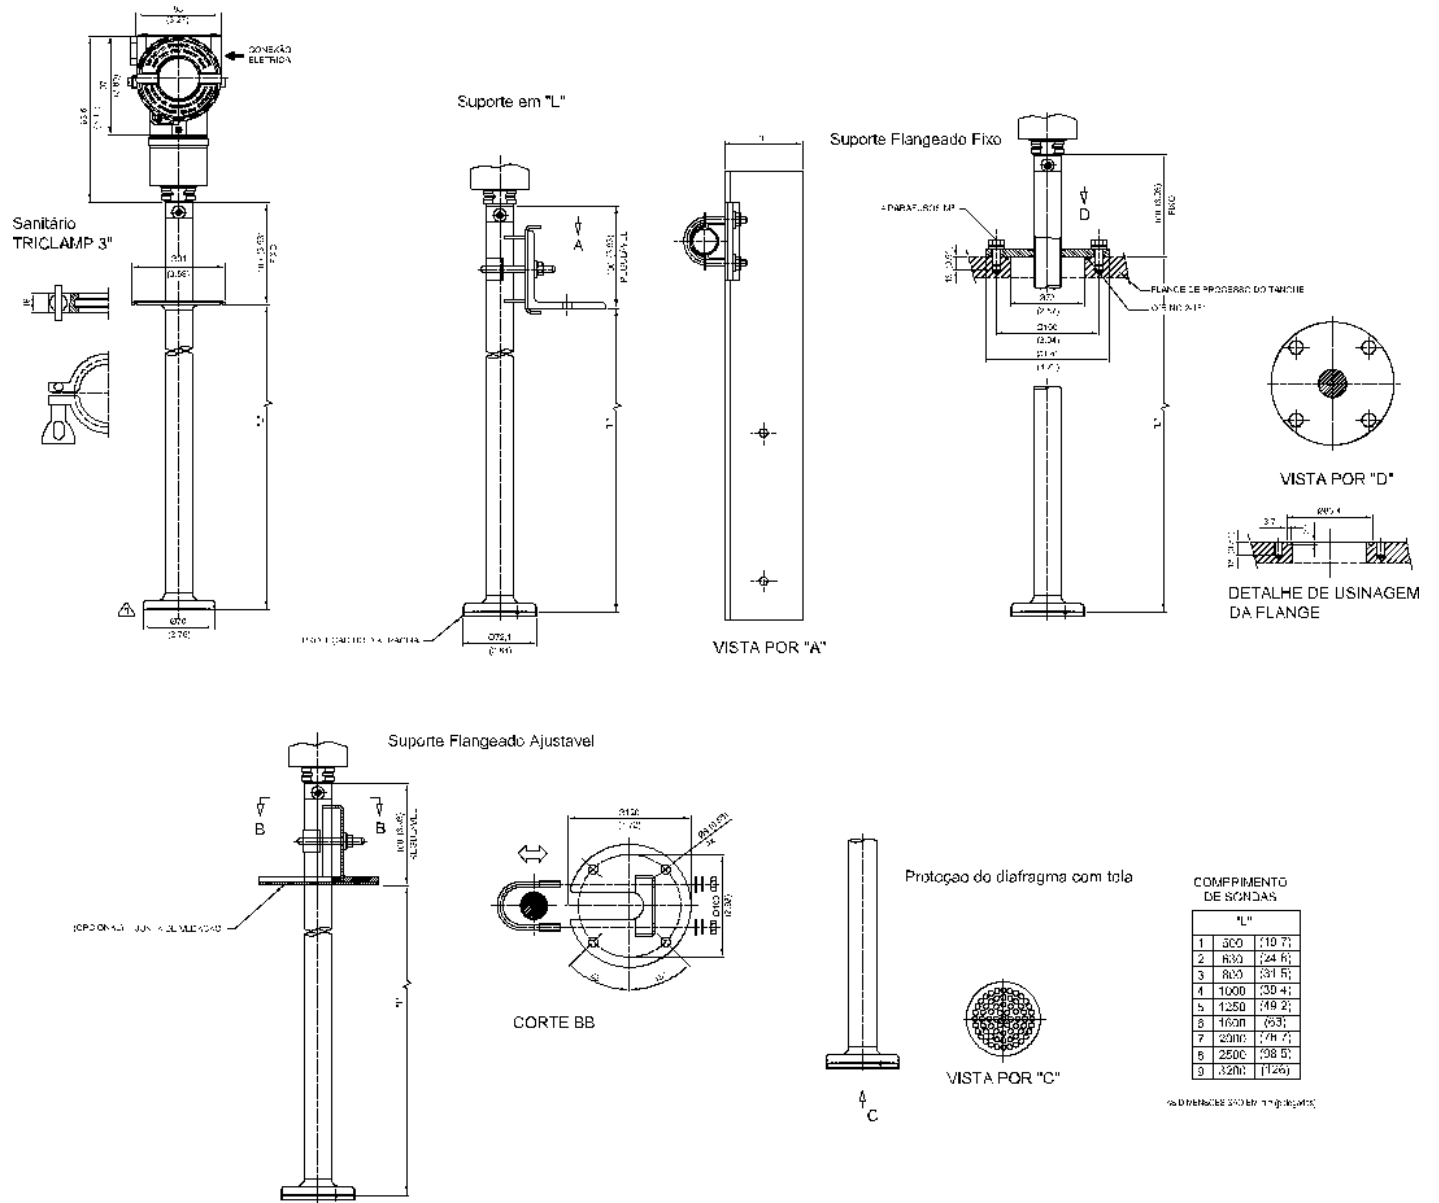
(d)- Desenho Dimensional de Montagem do LD291 – Nível (Inserção)
